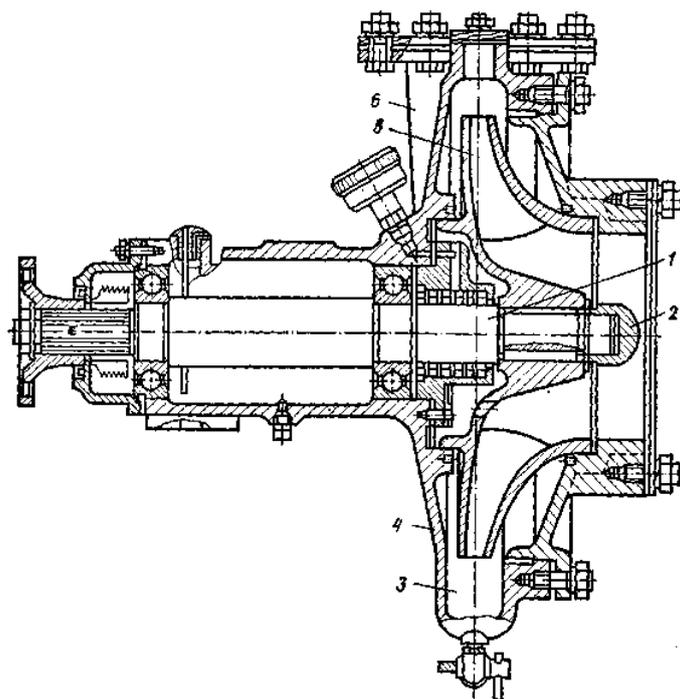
Пожарный насос ПН–60: 1 – вал; 2 – гайка; 3 – спиральная камера; 4 – корпус; 5 – рабочее колесо; 6 – диффузор
